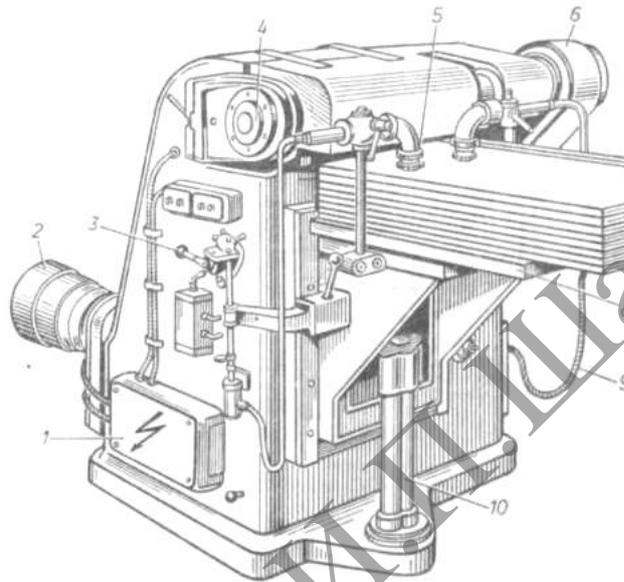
Двусторонний шипорезный станок ШД15-3
